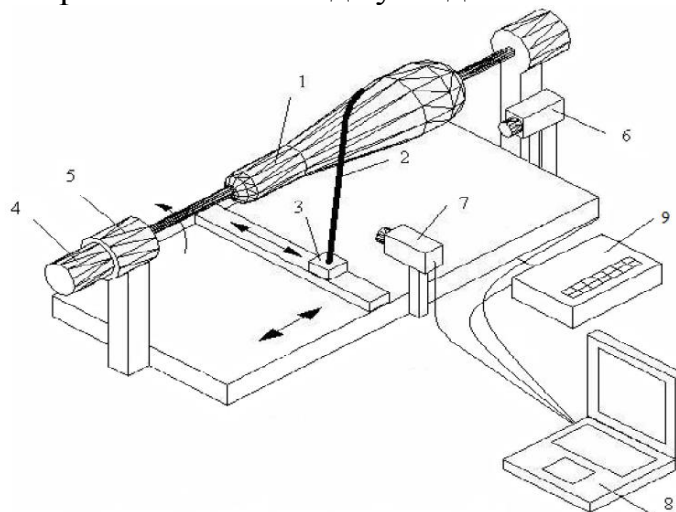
Принципиальная схема изготовления деталей методом сухой намотки: 1 – оправка; 2 – композиционная лента; 3 – раскладчик ленты; 4 - шаговый двигатель; 5 – редуктор; 6,7 – видеокамеры; 8 – компьютер; 9 – блок управления приводами
